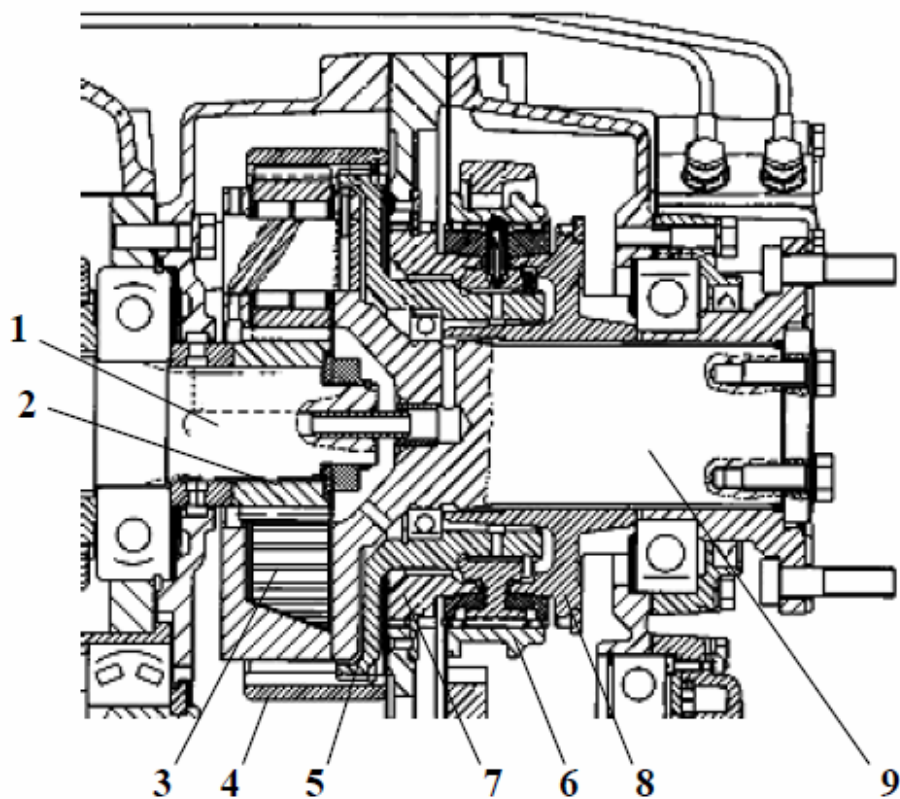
Продольный разрез демультипликатора коробки передач КАМАЗ модели 161. Расшифровка позиций – см. рис. 3.54
